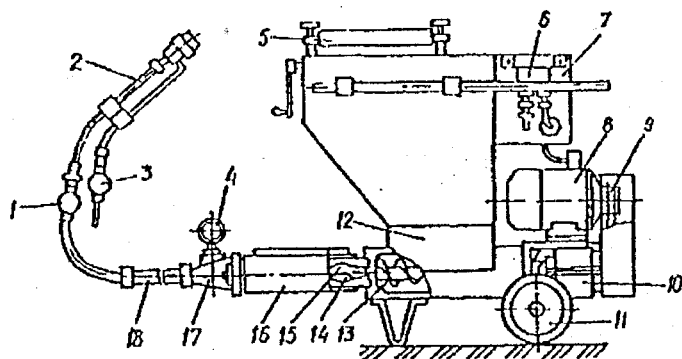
Шпаклювальний агрегат СО-150: 1,3 - крани; 2 - вудочка; 4 - манометр; 5 - витискальний пристрій; 6 - пневмореле; 7 - електрошафа; 8 - електродвигун; 9 - клинопасова передача; 10 - редуктор; 11 - колеса; 12 - завантажувальний бункер; 13 - гвинтовий конвеєр; 14 - статор; 15 - ротор; 16 - стінова обойма; 17 - наконечник; 18 - подавальний рукав
